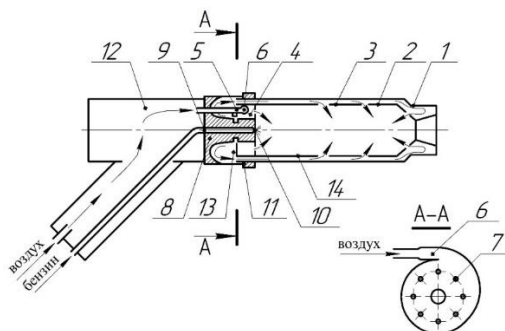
Термоотбойник с энергоразделителем: 1 – сопло; 2 – жаровая труба; 3 – кожух; 5 – вихревая камера; 6 – отверстия для прохода воздуха; 7 – наклонные отверстия; 8 – конус; 9 – центральный канал; 10 – форсунка; 11 – контргайка; 12 – рукоять
